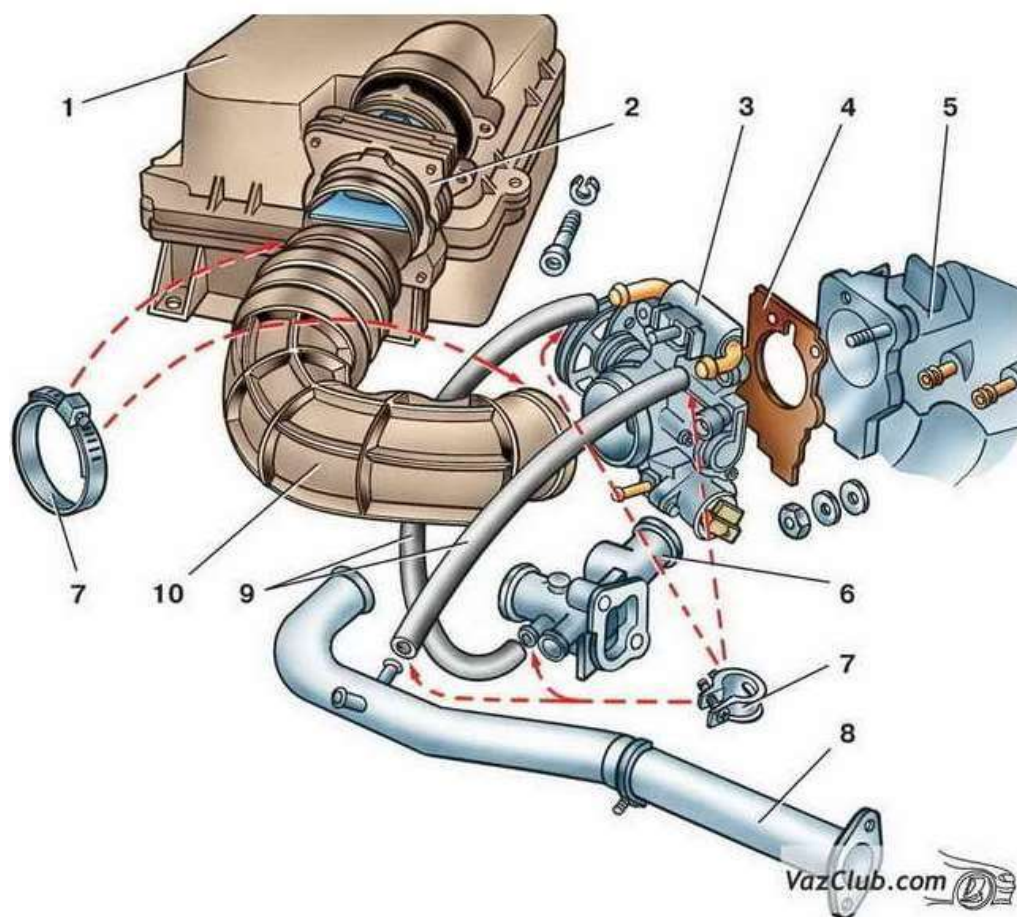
Снятие узлов и деталей системы подачи воздуха: 1 – воздушный фильтр; 2 – датчик массового расхода воздуха; 3 – дроссельный патрубок; 4 – уплотнительная прокладка; 5 – ресивер; 6 – выпускной патрубок системы охлаждения двигателя; 7 – хомуты крепления шлангов; 8 – подводящая труба насоса охлаждающей жидкости; 9 – шланги подогрева дроссельного патрубка; 10 – шланг впускной трубы
